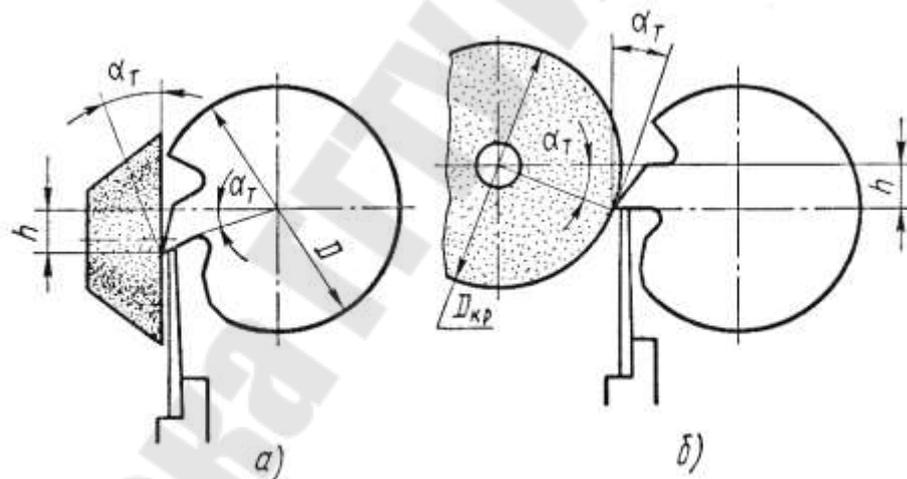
Установка абразивный инструмент при заточке задней поверхности обрабатываемого инструмента: торцом круга (а), периферией круга (б).
